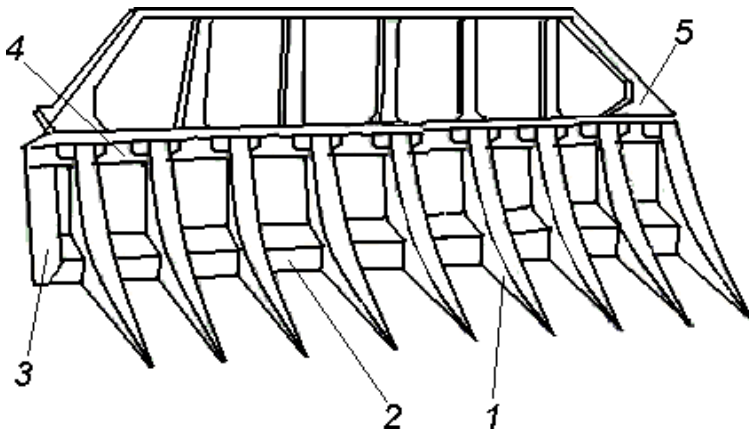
Решётчатый отвал корчевателя-собираеля: 1 – корчующие зубья; 2 – опорный брус; 3 – боковая стенка; 4 – несущий брус; 5 – защитная решётка
